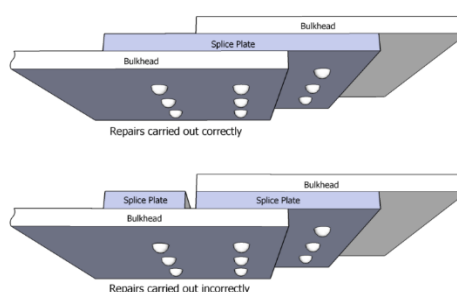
Instalações corretas (superiores) e incorretas da placa de emenda.
